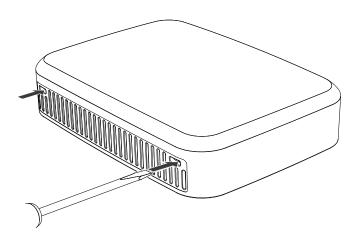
Desmontaje tapa frontal / Front cover dismounting / Démontage du couvercle / Smontaggio coperchio frontale / Demontage voorklep / Odejmutí předního krytu
